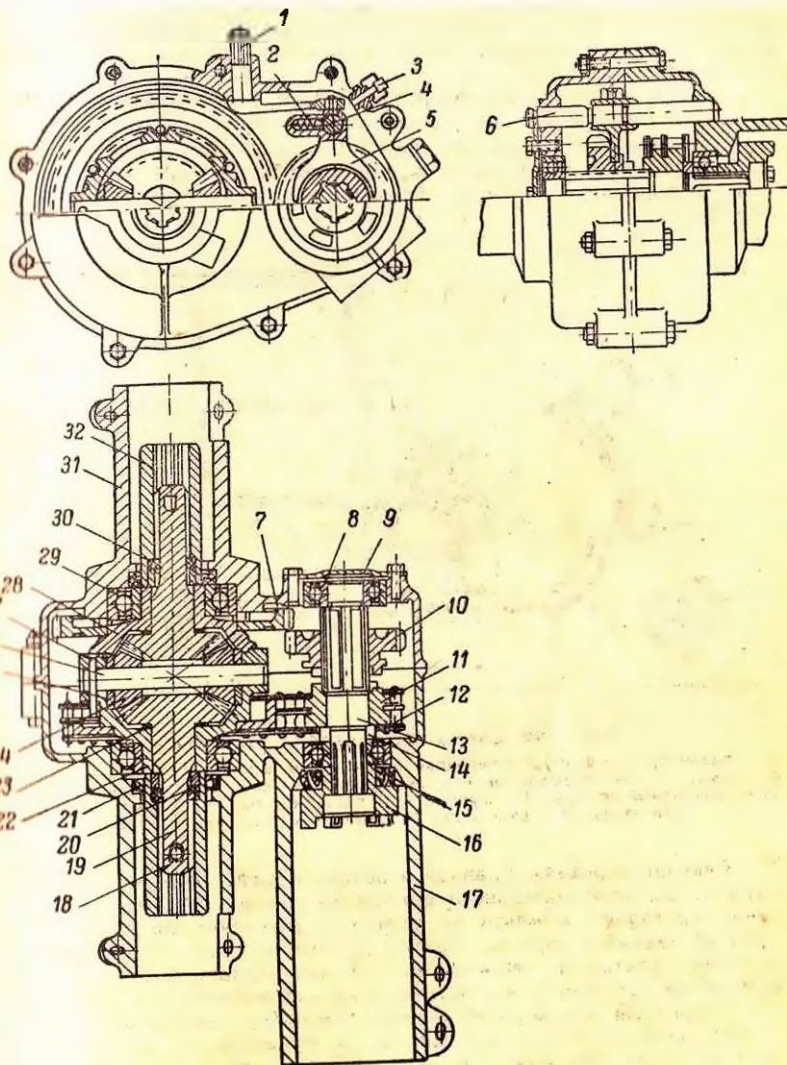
Главная передача грузового мотороллера „Вятка“:
